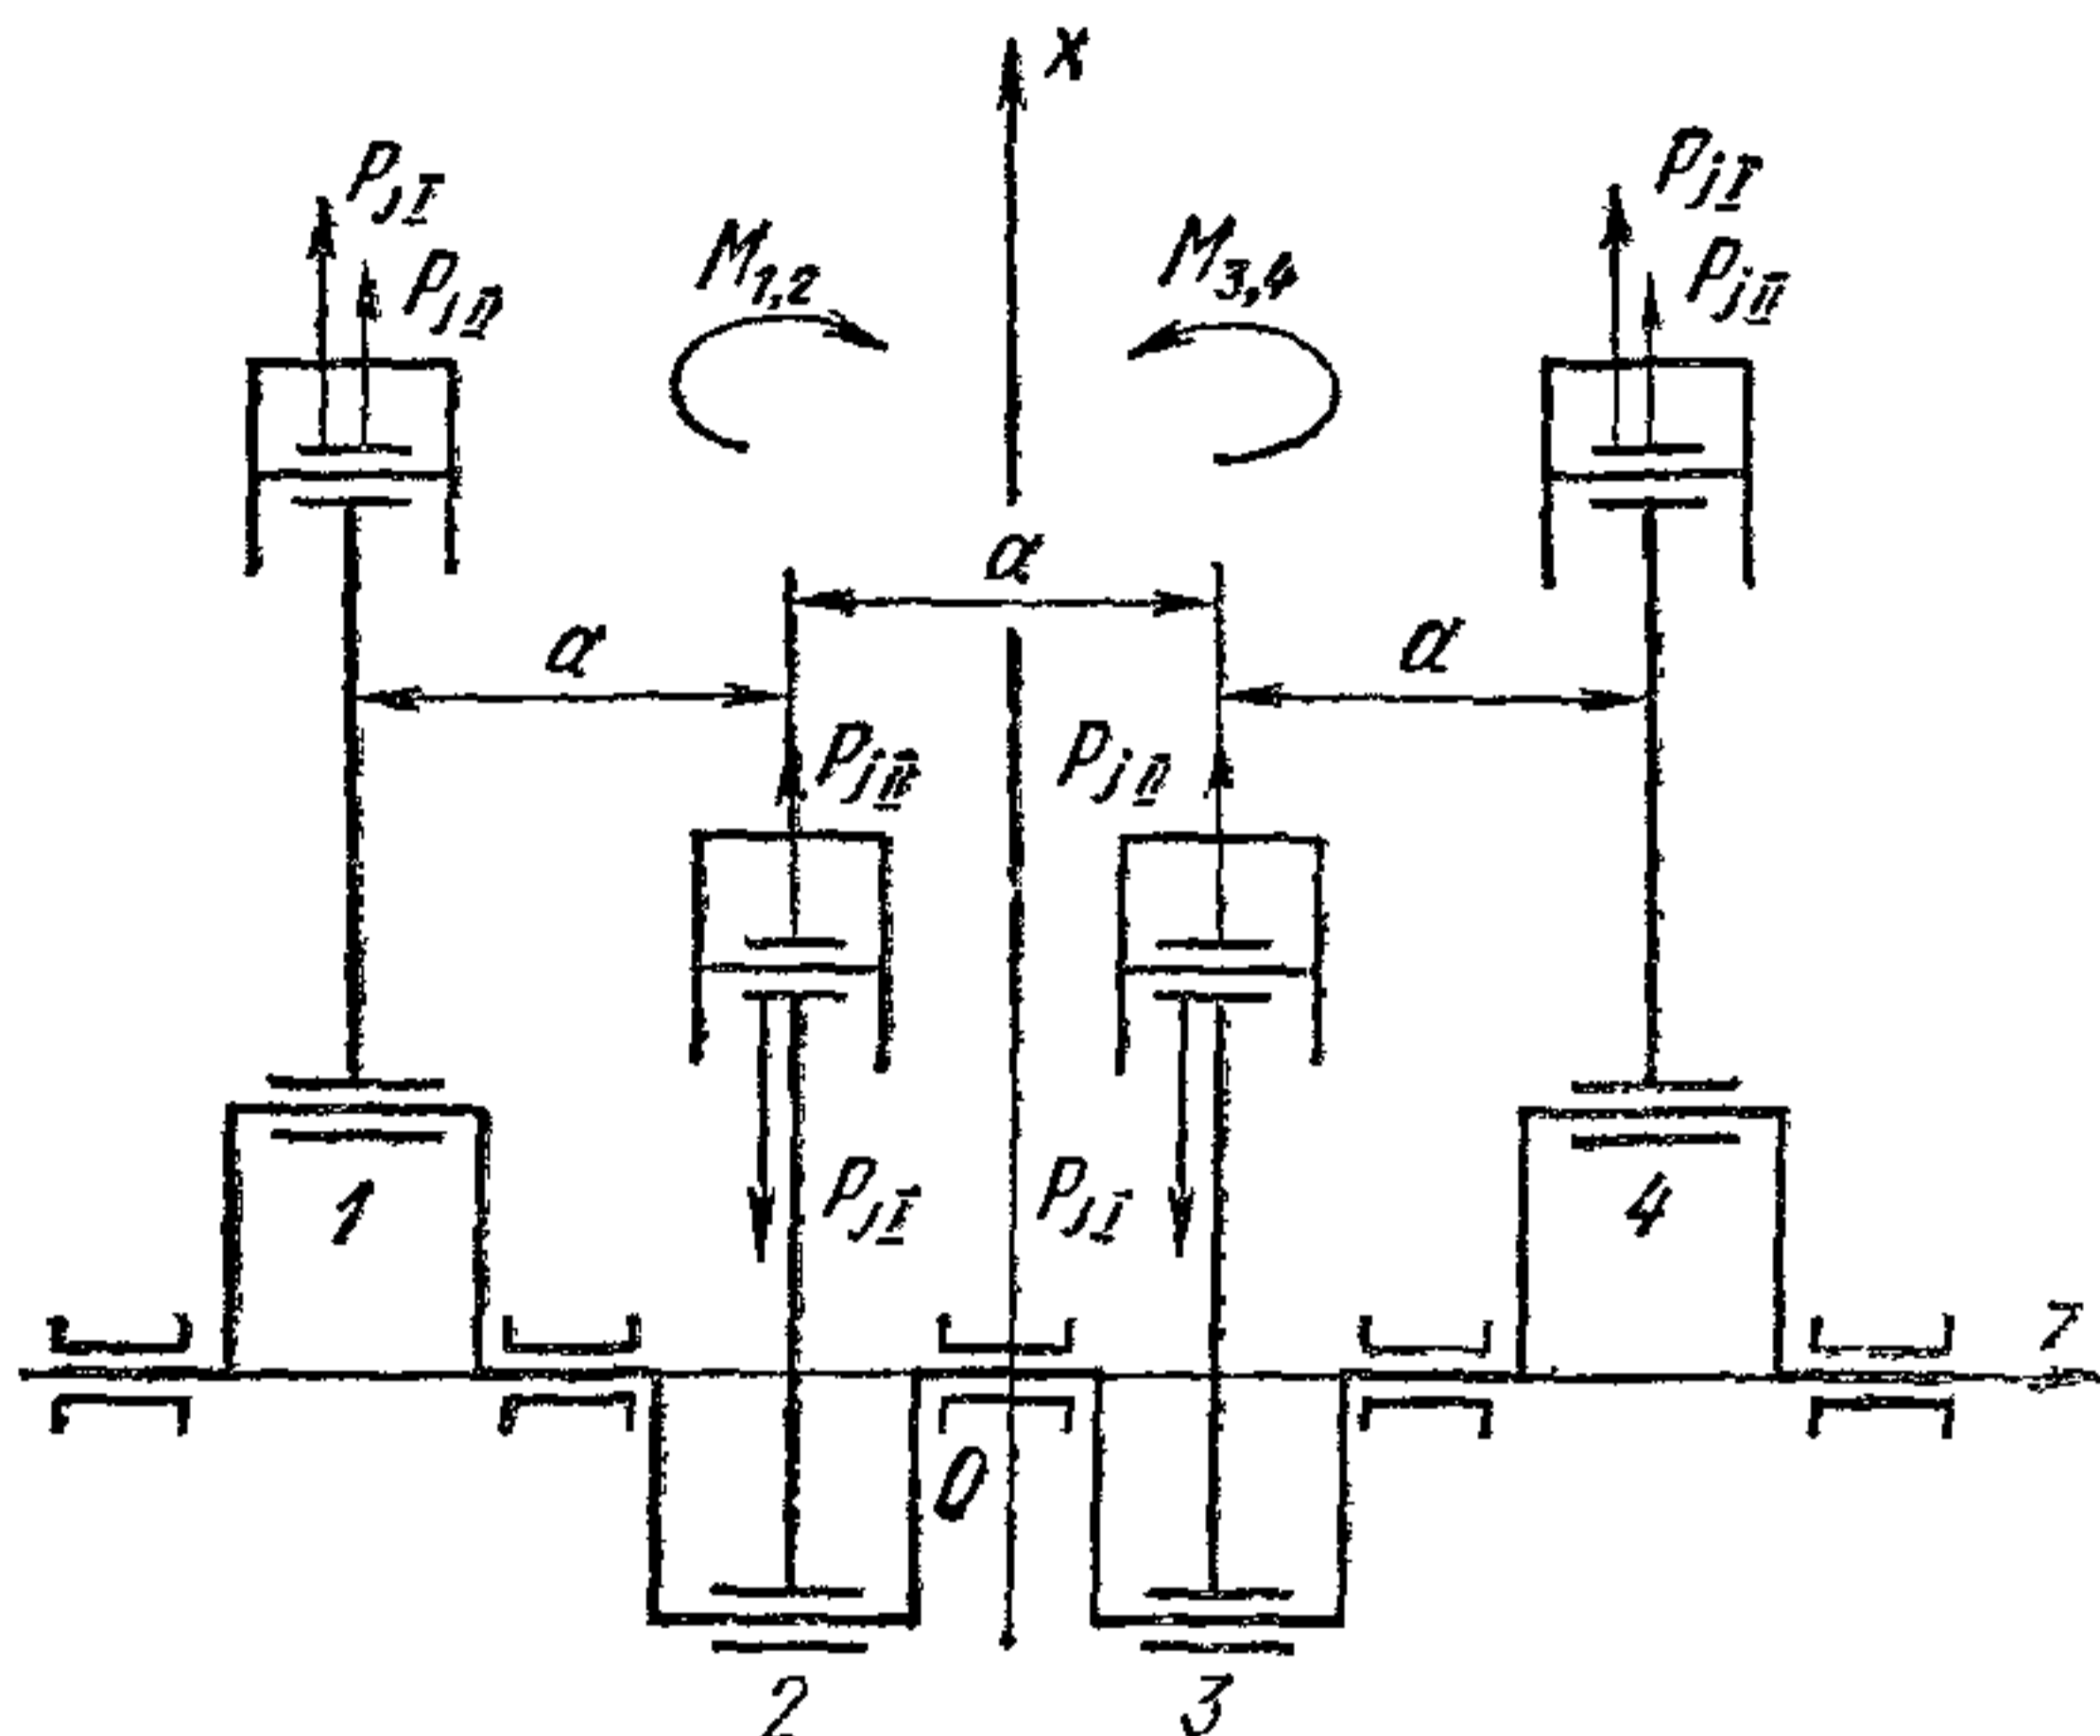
Схема коленчатого вала однорядного четырехцилиндрового, четырехтактного двигателя
